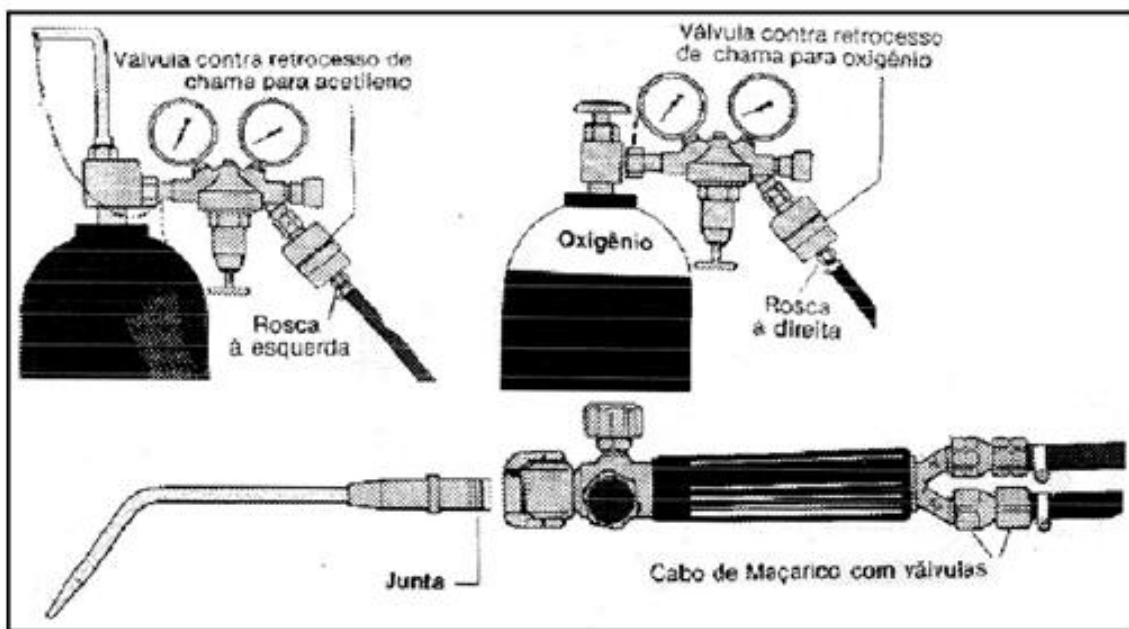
Equipamento utilizado no processo de soldagem oxi-acetilênico.
